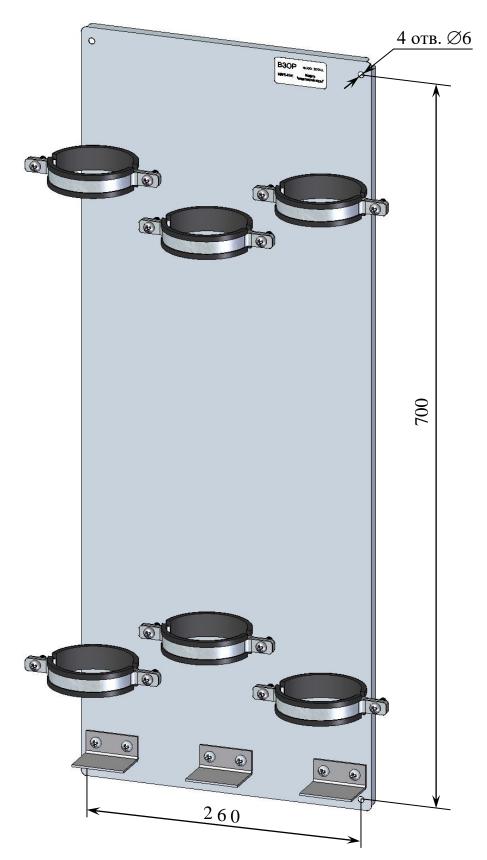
Расположение и размер отверстий для крепления панели модуля
